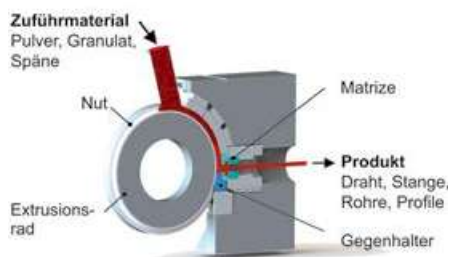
Temconex®-Schema: Extrusionsrad und Werkzeugschuh bilden einen Extrusionskanal, zugeführtes Metallpulver verschweißelt aufgrund von Reibung ohne Aufschmelzen und wird zu einem Draht extrudiert.
